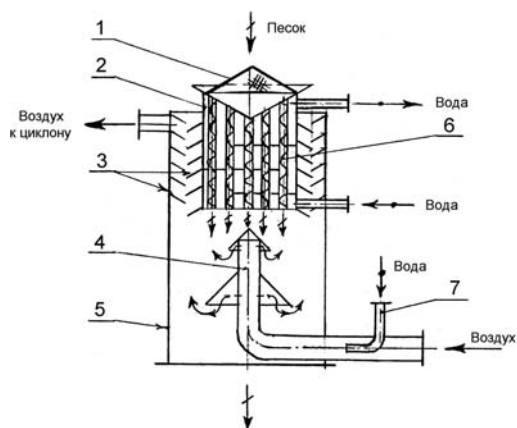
Установка охлаждения сыпучего формовочного материала комбинированным способом. 1 – сетчатый колпак, 2 – водоохлаждаемый корпус, 3 – отражающие пыль кольца, 4 – воздухоподводящий патрубок, 5 – наружный корпус.
